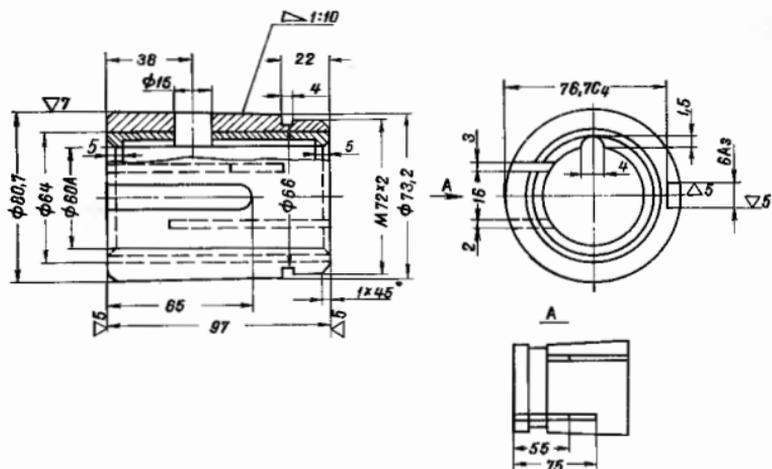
Подшипник серги. Деталь 2-72×2 Су-III
